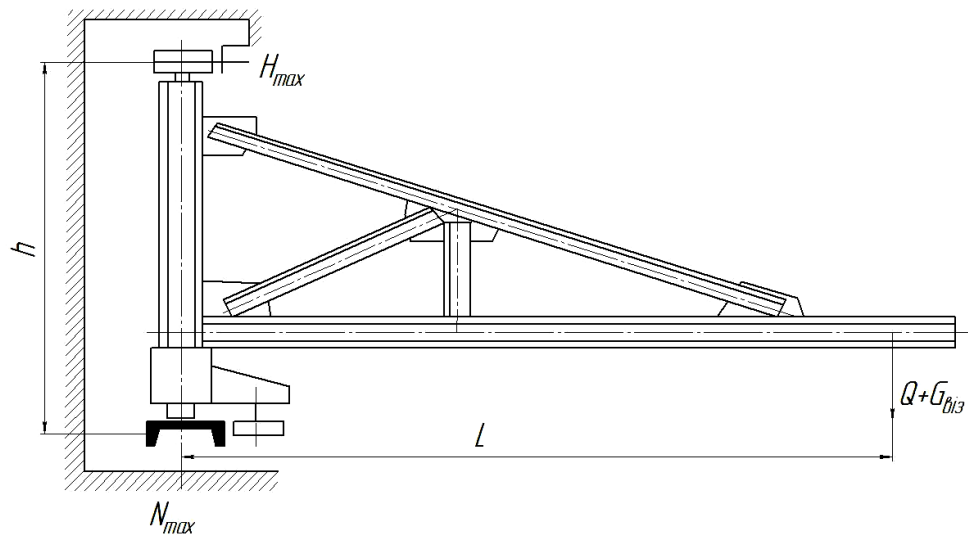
Настінний поворотний консольний кран з їздою "по низу".
